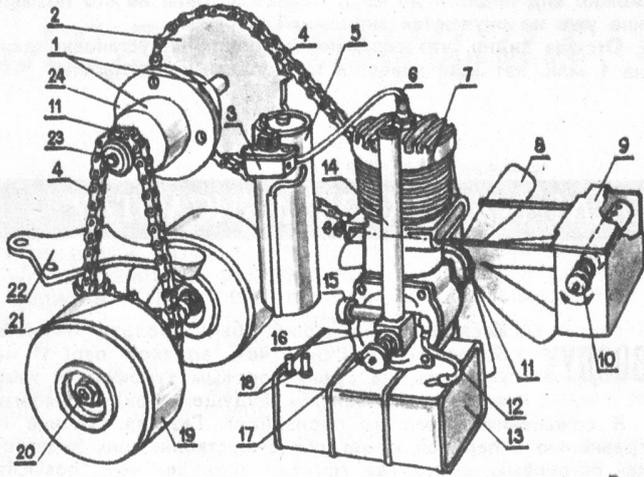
Двигатель: 1 — подшипник, 2 — зубчатка (32 зуба), 3 — включатель зажигания, 4 — цепь, 5 — батарея зажигания, 6 — фильтр, 7 — мотор на 10 см³ со свечой, 8 — вентилятор, 9 — задвижка выхлопного канала (латунь 2 мм, размеры 25×30×75 мм), 10 — регулирующий затвор задвижки, 11 — цепное колесо (10 зубцов), 12 — пластмассовая трубка для впуска горячего, 13 — бачок для горячего (30×45×75 мм), 14 — канал для впуска воздуха, 15 — маховичок регулятора впуска горячего, 16 — латунный карбюратор (см. также деталь А), 17 — маховичок регулятора впуска воздуха, 18 — трубка для наполнения бачка, 19 — система передних колес, 20 — ступица с подшипником, 21 — цепное колесо (10 зубцов), 22 — подножка от колесного конька, 23 — вал, 24 — оправка.
